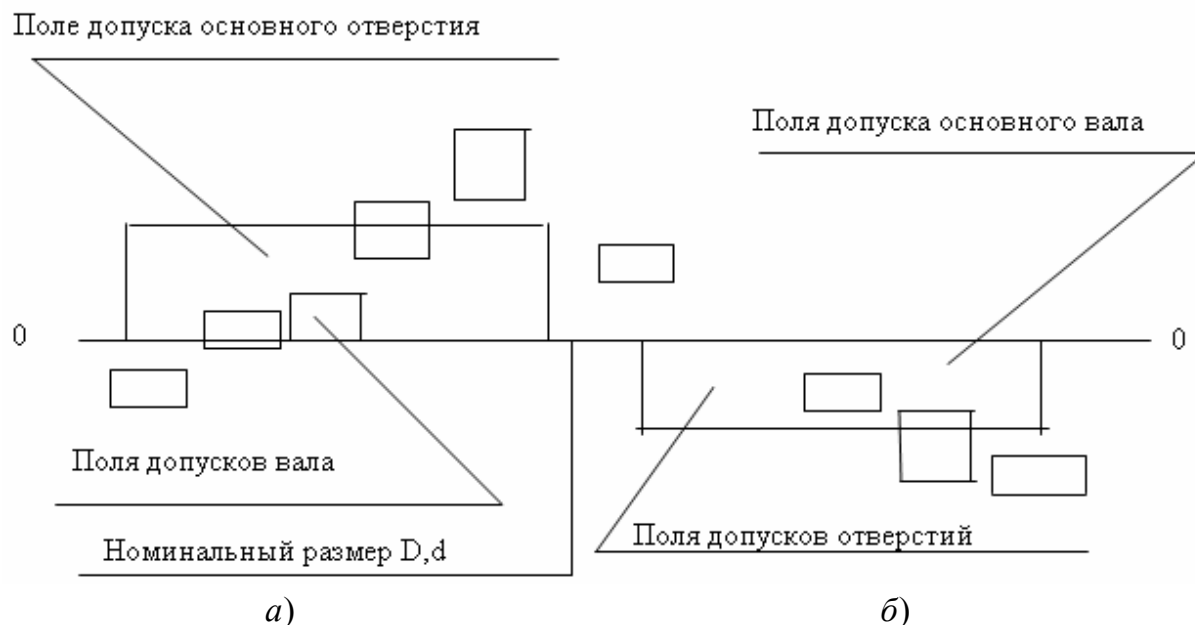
Примеры расположения полей допусков для посадок в системах отверстия (а) и вала (б)
